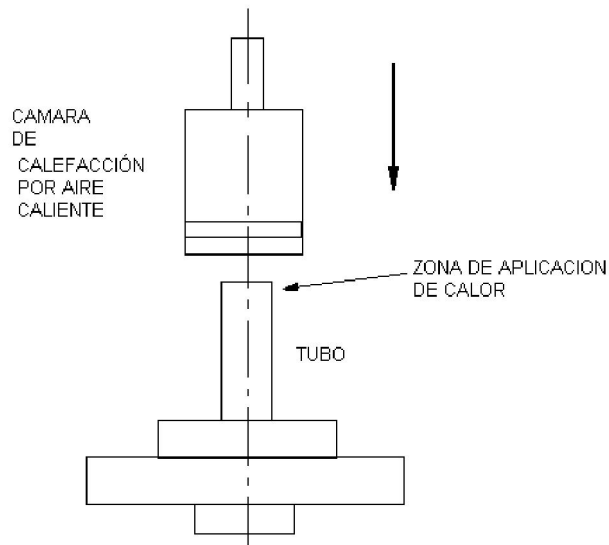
Esquema de soldadura por aire caliente
